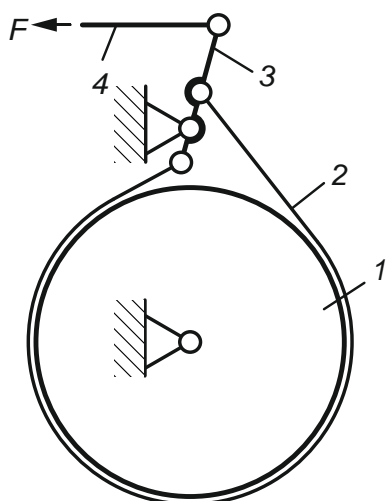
Схема барабанно-ленточного тормозного механизма:
